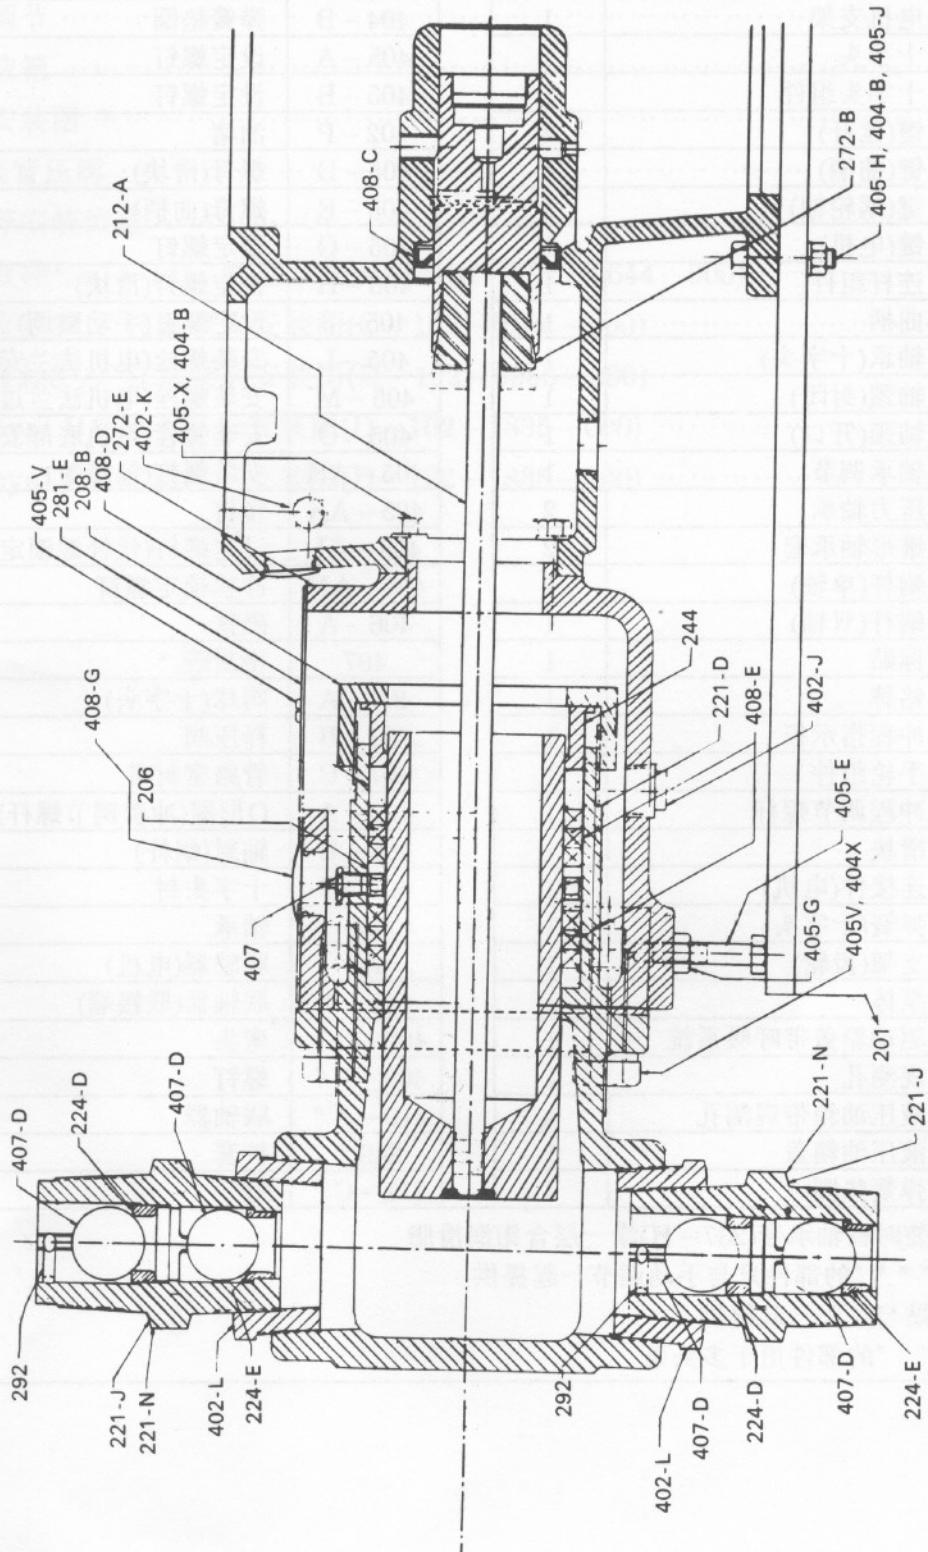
3 1/2"柱塞泵头安装图(D-102-0955-000)
